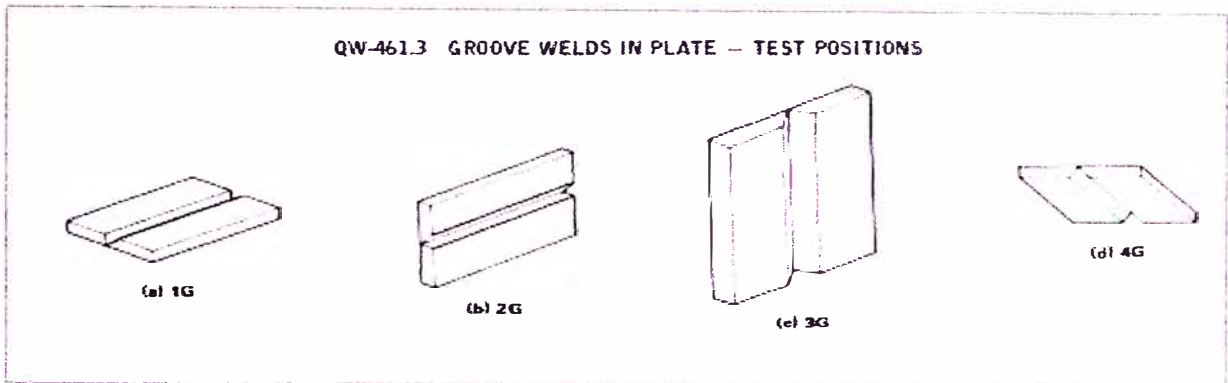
posiciones de prueba en planchas y Tubos – Juntas a Tope.
